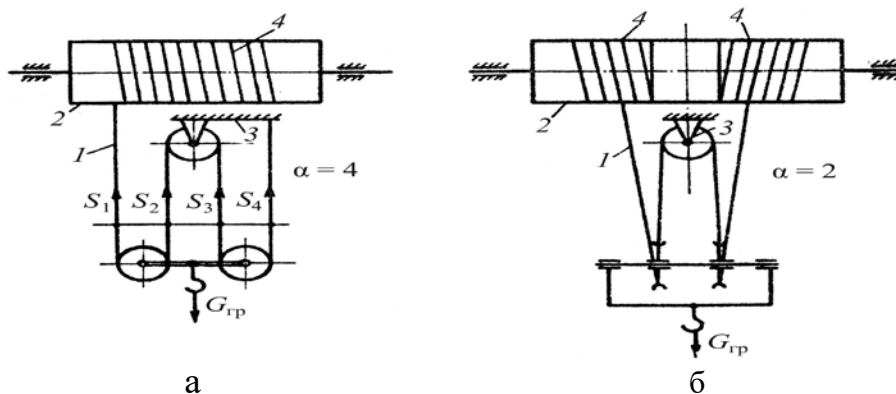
Полиспасты: а – одинарный: 1 – канат, 2 – барабан, 3 – неподвижная часть конструкции грузоподъемные машины 4 – нарезка барабана; б – сдвоенный: 1 – канат, 2 – барабан, 3 – уравнительный блок, 4 – встречная нарезка барабана.
